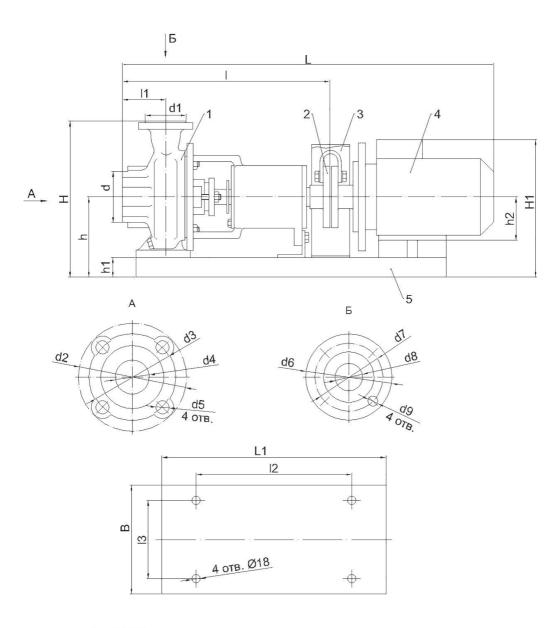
Габаритные и присоединительные размеры насоса 1 - насос; 2 - муфта; 3 - кожух; 4 - электродвигатель; 5 - плита
